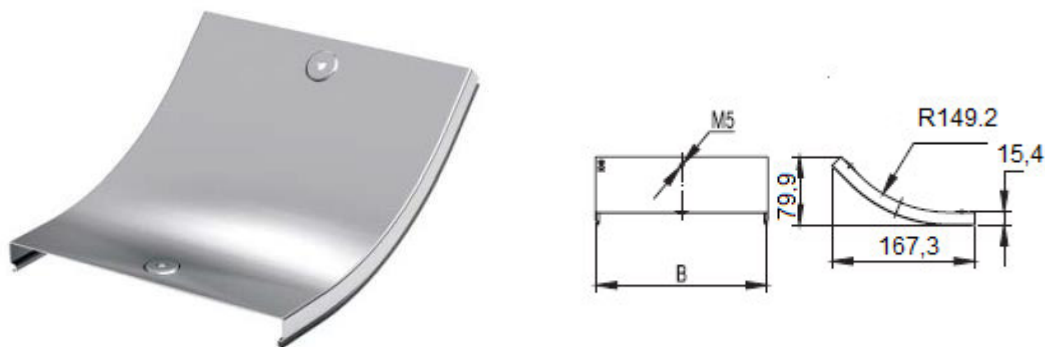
Крышка CS 45 на угол вертикальный внутренний 45°, тип 3822
